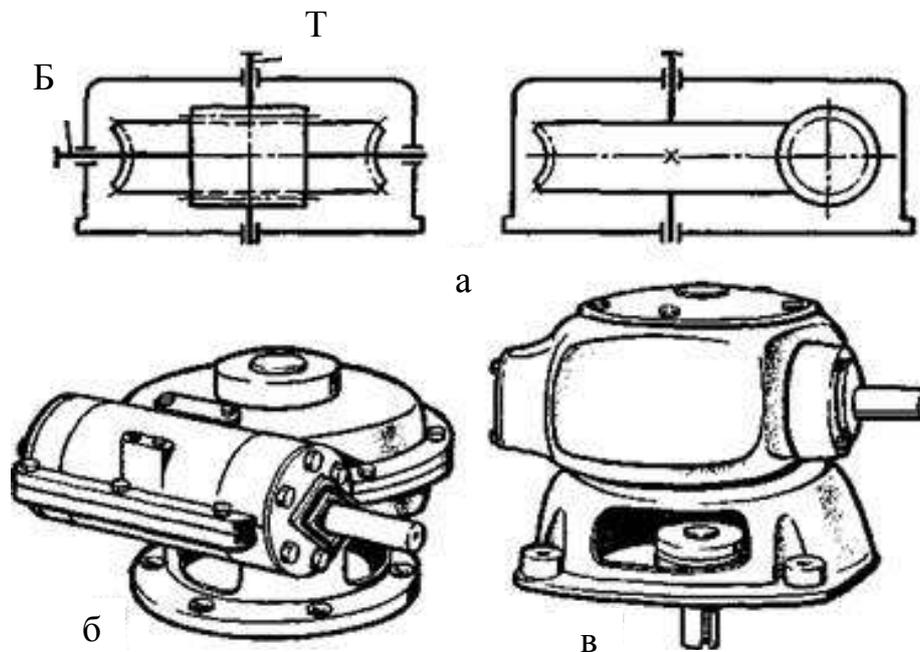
Червячный редуктор с вертикальным валом червячного колеса: а – кинематическая схема; б – общий вид редуктора с разъемным корпусом; в – общий вид редуктора с неразъемным корпусом
